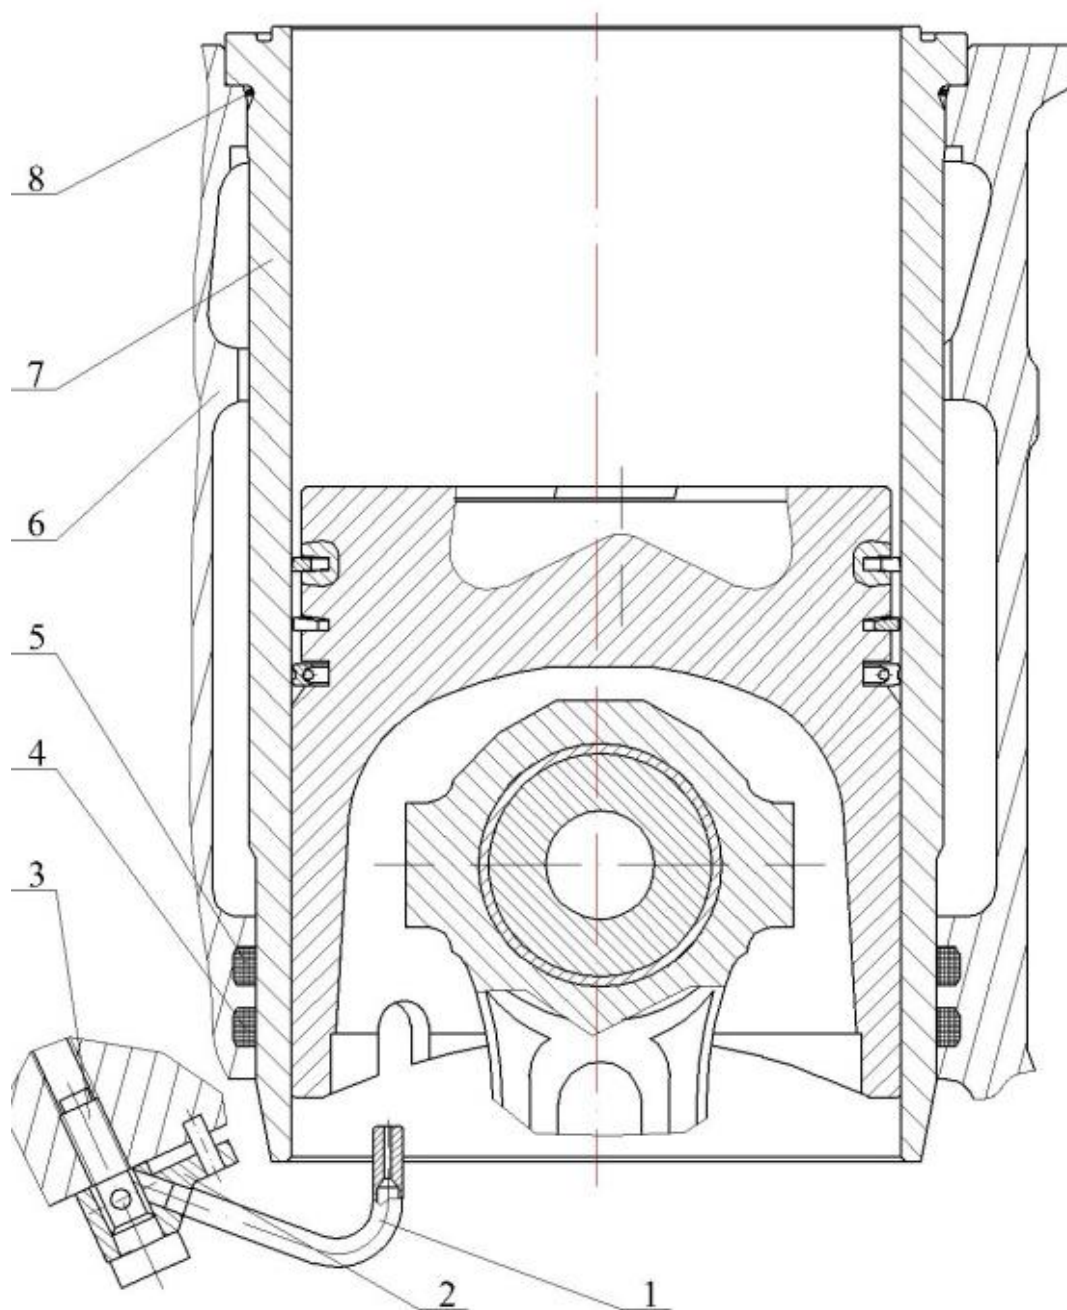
Установка гильзы цилиндра и уплотнительных колец:
